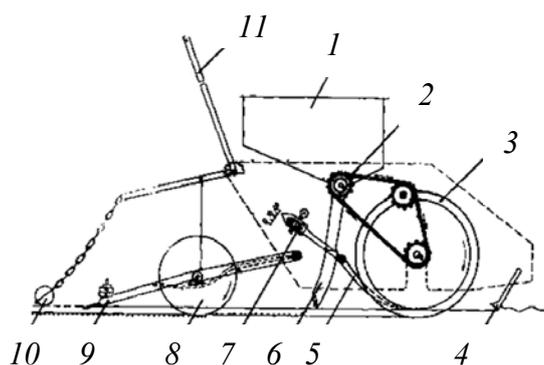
Схема сеялки «Литва-25»: 1 – бункер для семян; 2 – лопастно-ячеистый высевующий валик; 3 – бороздообразующий каток; 4 – нож-планировщик; 5 – очистительная расческа; 6 – пятиотсечный семяпровод; 7 – винтовой регулятор; 8 – вдавливающий каток; 9 – секции заделки семян; 10 – волокуша; 11 – рычаг
